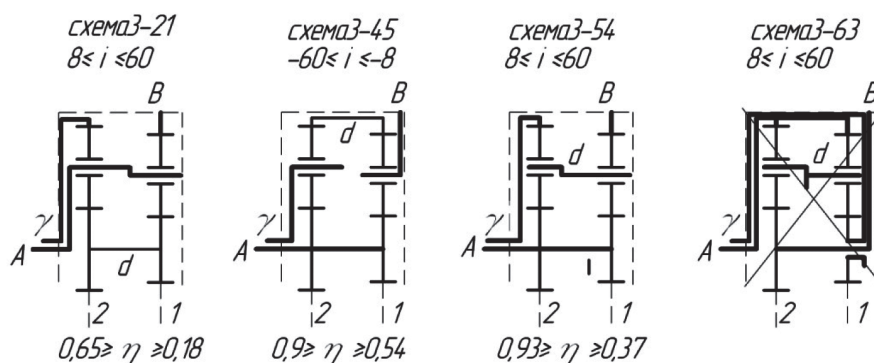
Кинематические схемы встроенного редуктора по схеме 3 с расположением быстроходной ступени 1 со стороны, противоположной входу
